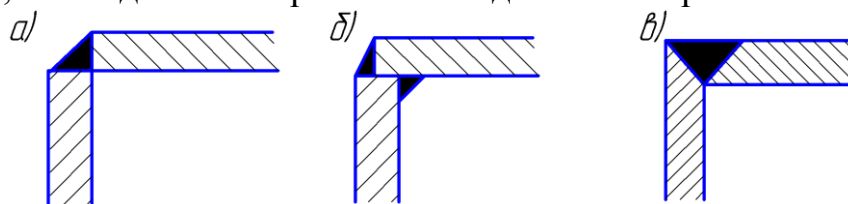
Угловые сварные соединения: а) односторонние без подготовки кромок; б) двухсторонние без подготовки кромок; в) односторонние с подготовкой кромок.
